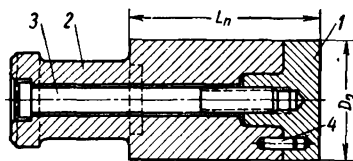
Сборный обрезной пуансон ( $D_n = 80 \div 160$  мм): 1 — пуансон; 2 — державка; 3 — винт; 4 — штифт
